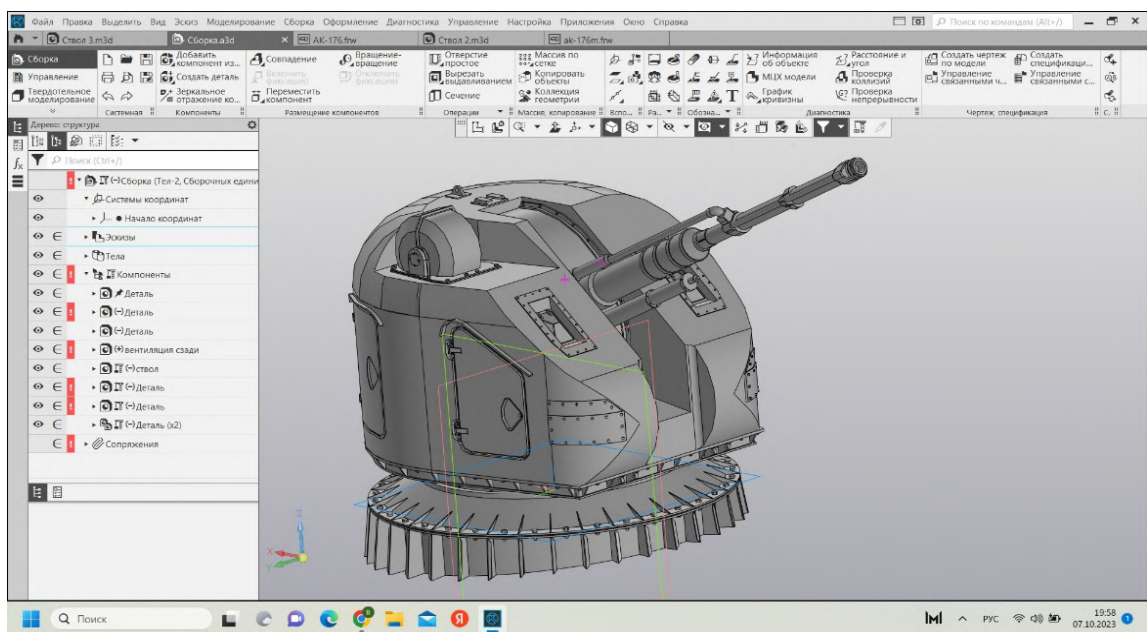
3D-модель артиллерийской установки АК-176.
